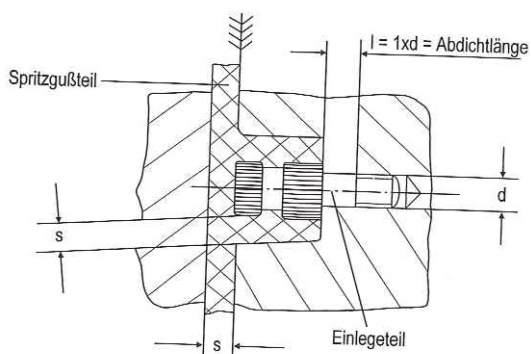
Eingebetteter Stift mit Rändelung und Ringnut. Der Stift selber wird vor dem Schließen des Werkzeugs in einer Werkzeugseite in einer Bohrung aufgenommen. [3]
